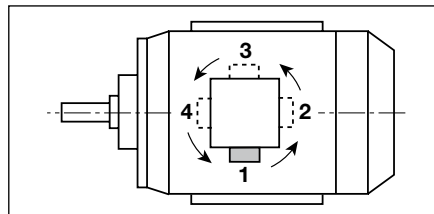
U - Orientamento dell'entrata cavi vista in pianta
